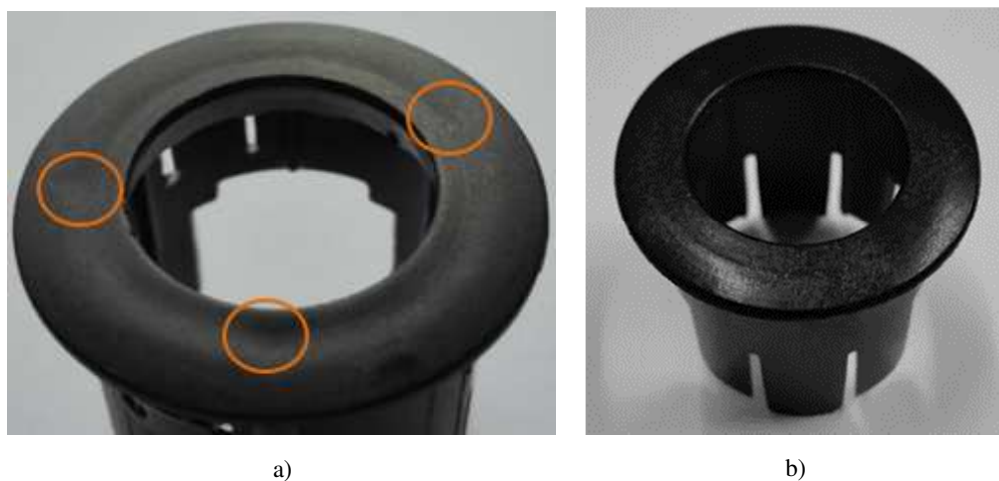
Sensor housing*: molde de fabrico convencional (a); molde de fabrico aditivo (b)
